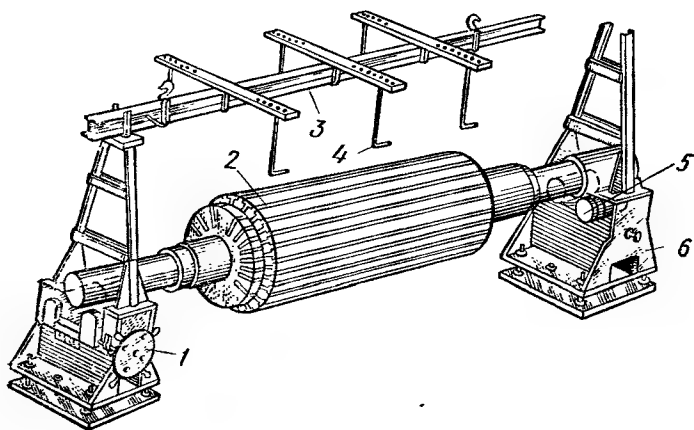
Приспособление для укладки обмотки ротора турбогенератора
